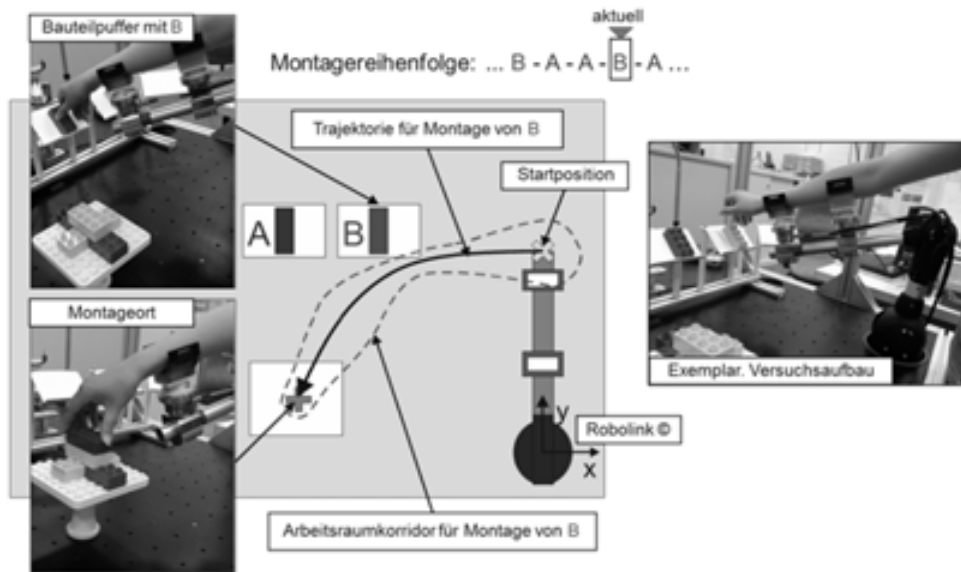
Baugruppenmontage mit zwei Bauteilarten nach einer festgelegter Montagereihenfolge
